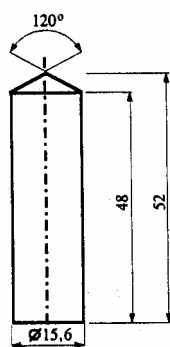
Pistón cilíndrico de bronce, dimensiones en mm.
